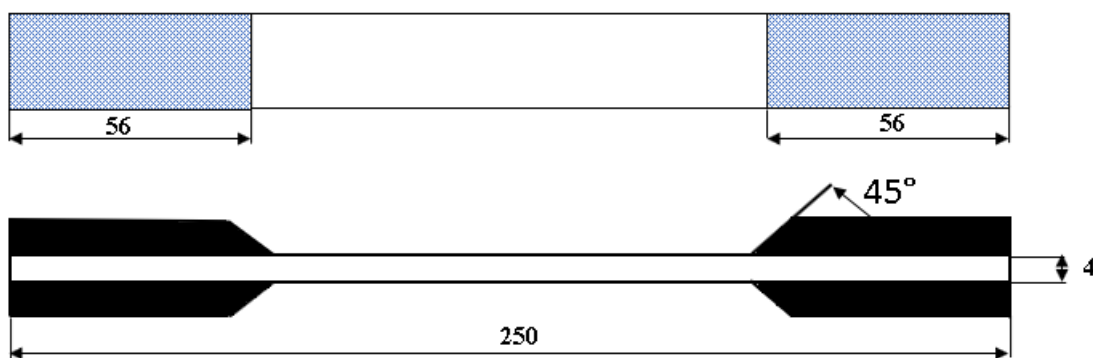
Dimensiunile epruvetei GFRP conform ASTM D3039
